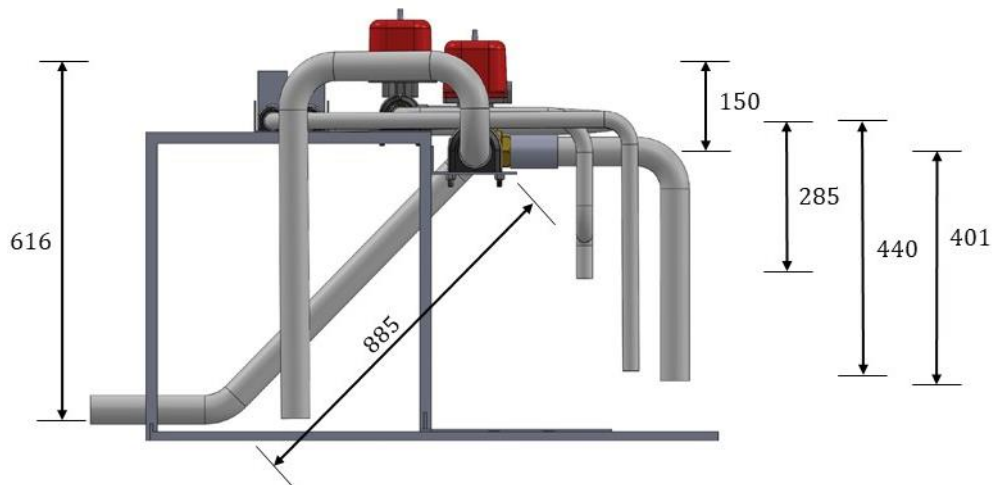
Comprimento aproximado de canalização no plano vertical (medidas em mm).
